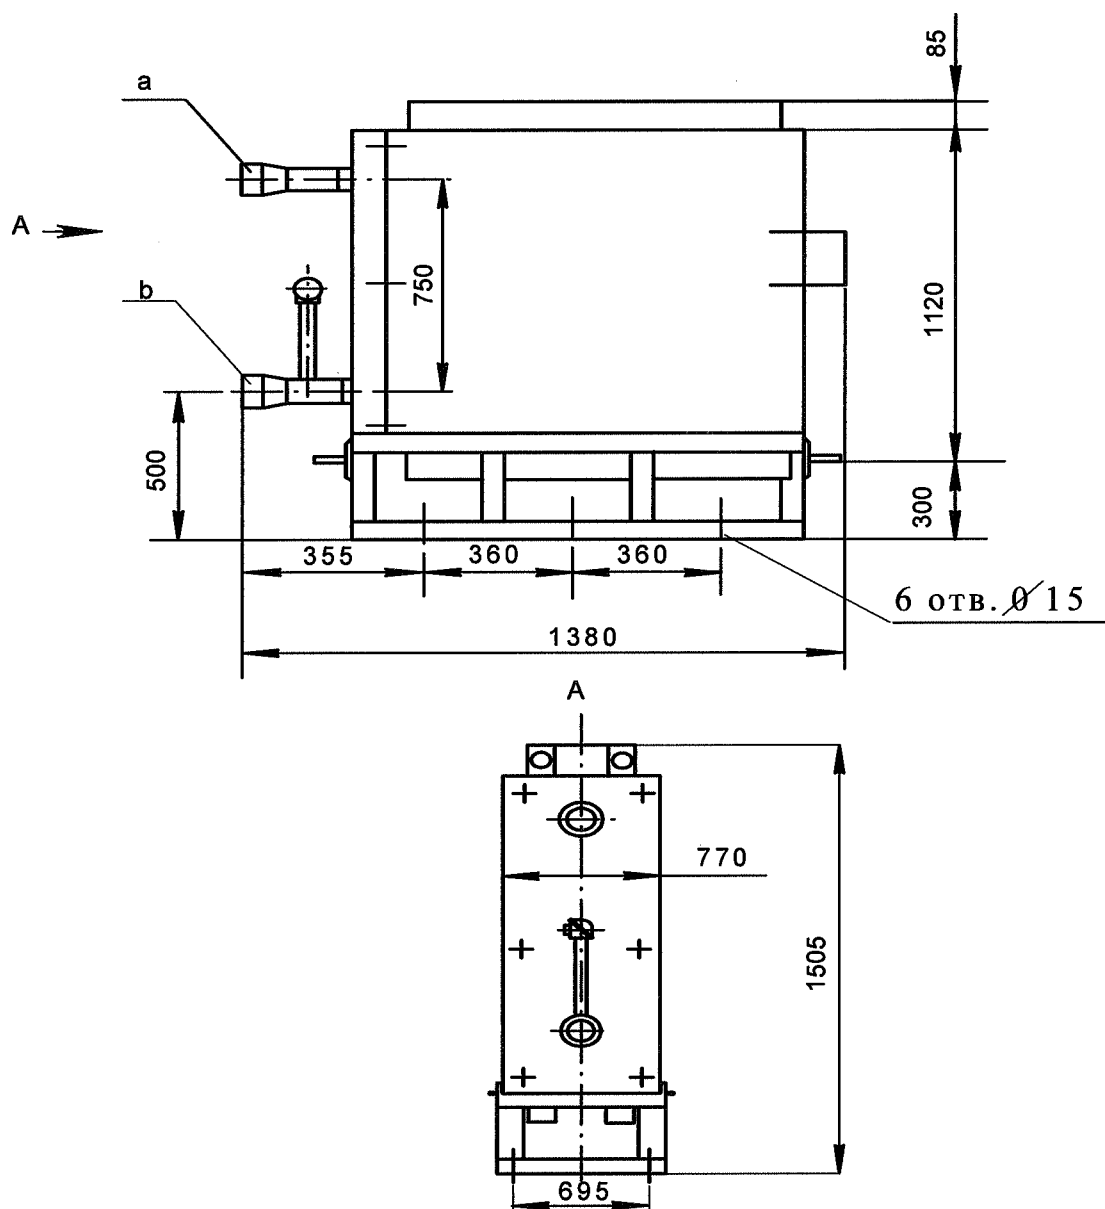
Габаритный чертеж электронагревателя KPL70AH001, KPL70AH002
